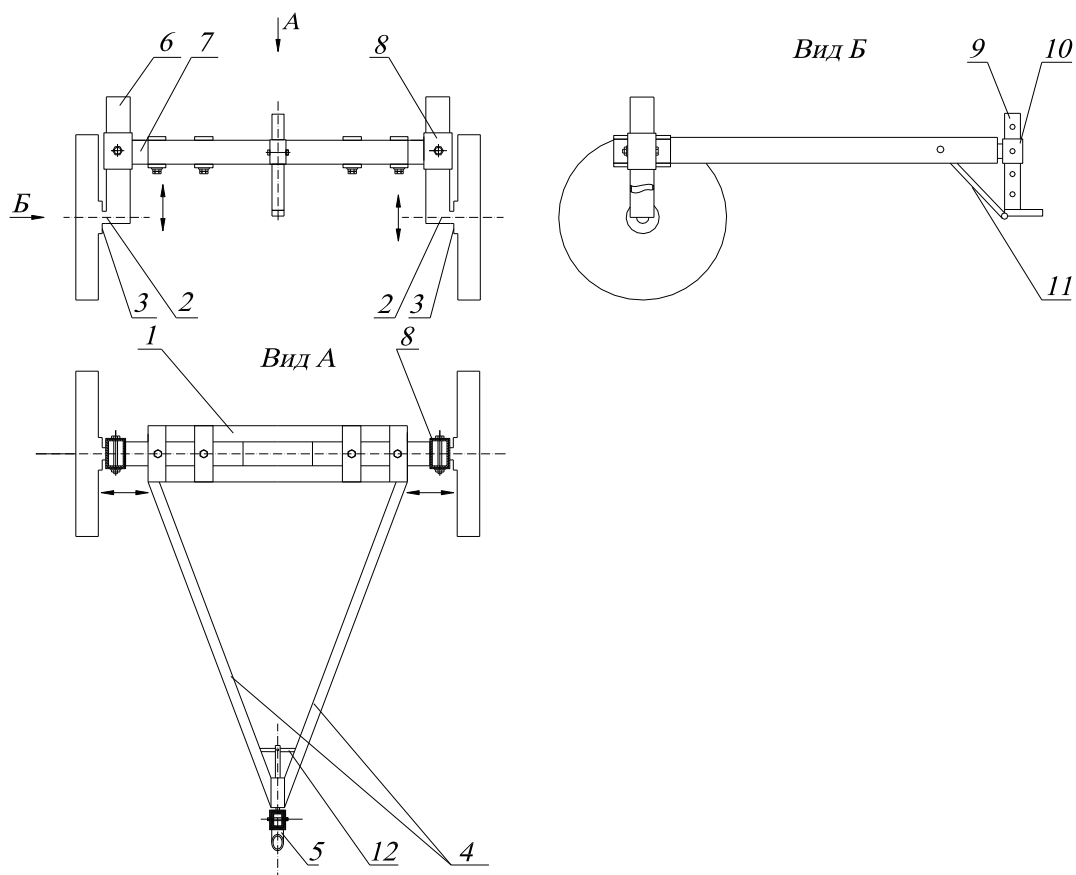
Несуча рама малогабаритного обприскувача
